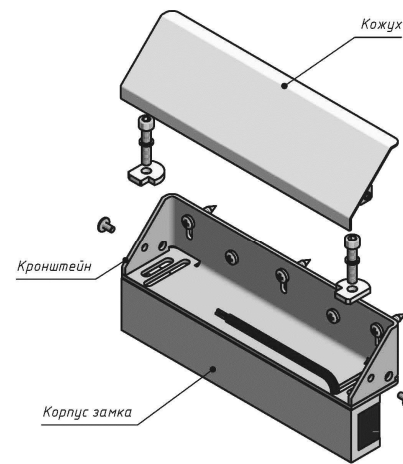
Крепление корпуса замка с помощью монтажного комплекта МК AL-350FB-M-01
